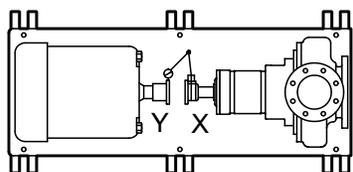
Vista dall'alto di un allineamento orizzontale scorretto
